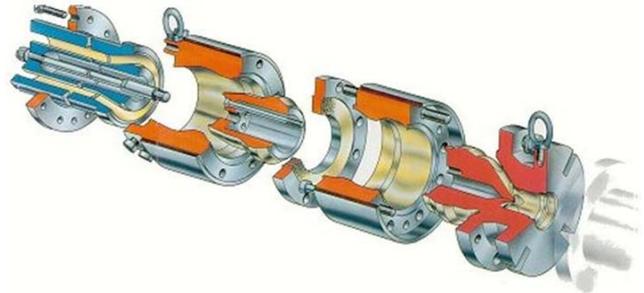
Werkzeuge mit Spinnenverteilern und Lochplatten (Krauss-Maffei)
